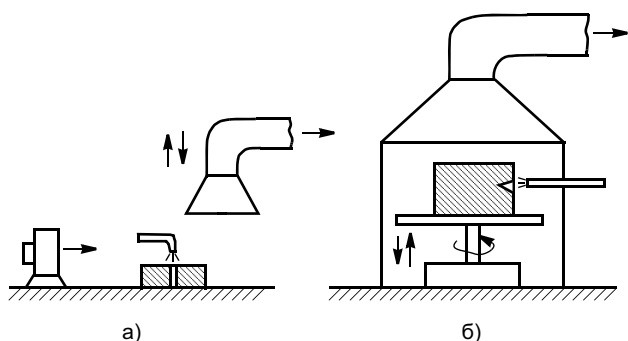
Вытяжное устройство разделки металлолома: а — вытяжной зонт; б — камера-укрытие для механизированной резки
